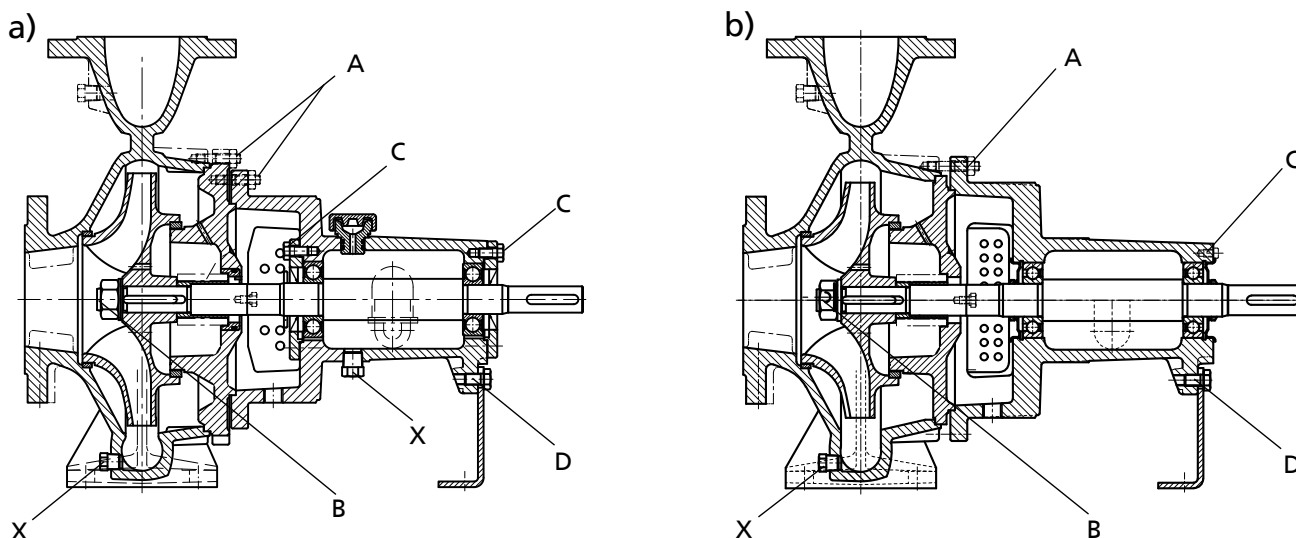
Позиции затяжки: Исполнение с резьбовой напорной крышкой (а) и масляной смазкой (а) и исполнение с зажимной напорной крышкой (b) и консистентной смазкой (b)
